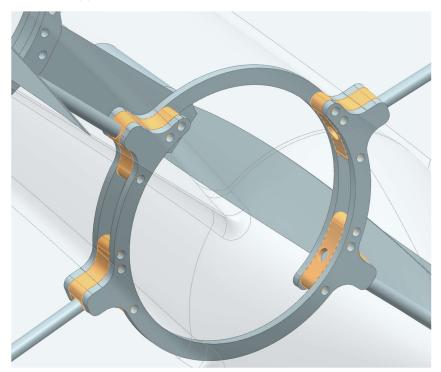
Резьбовые элементы, изготовляемые из металла
